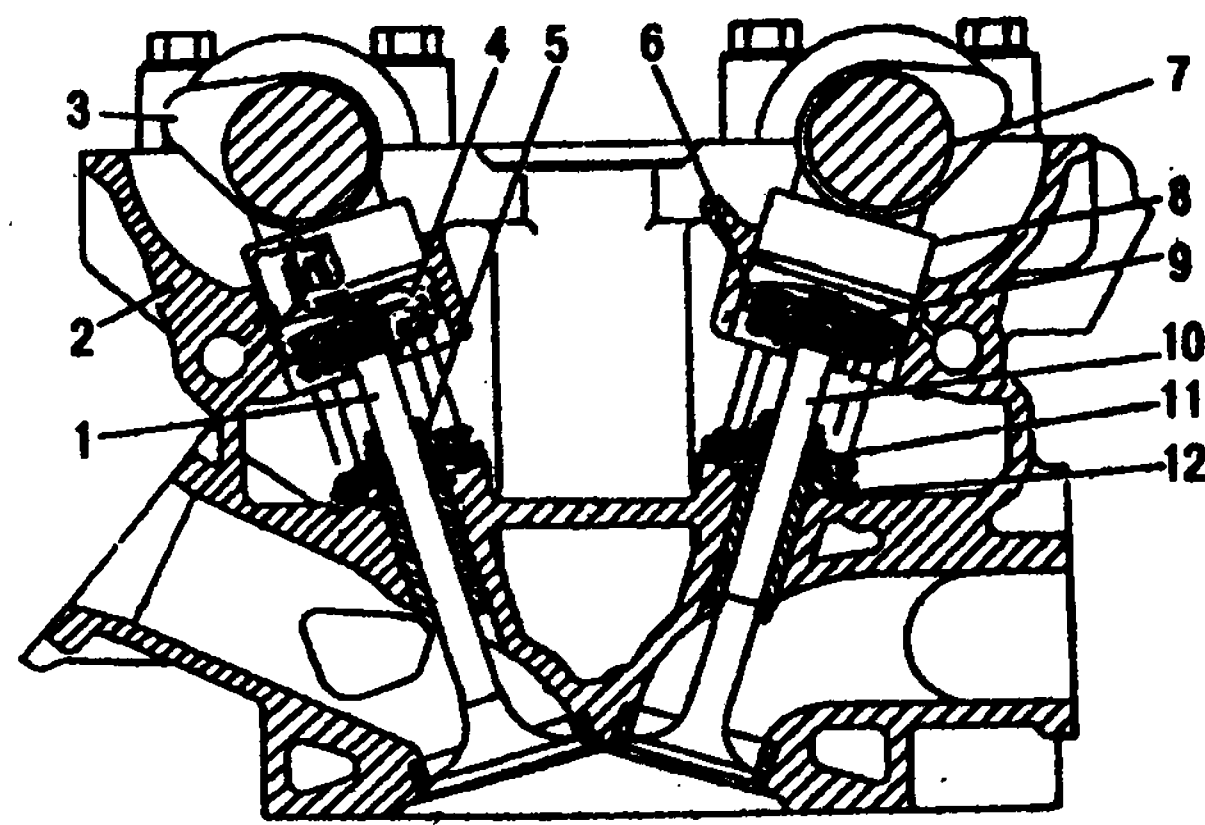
Привод клапанов: 1 - впускной клапан; 2 - головка цилиндров; 3 - распределительный вал впускных клапанов; 4 - тарелка пружин клапана; 5 - маслоотражательный колпачок; 6 - наружная пружина клапана; 7 - распределительный вал выпускных клапанов; 8 - гидротолкатель; 9 - сухарь клапана; 10 - выпускной клапан; 11 - внутренняя пружина клапана; 12 - опорная шайба пружин клапана
